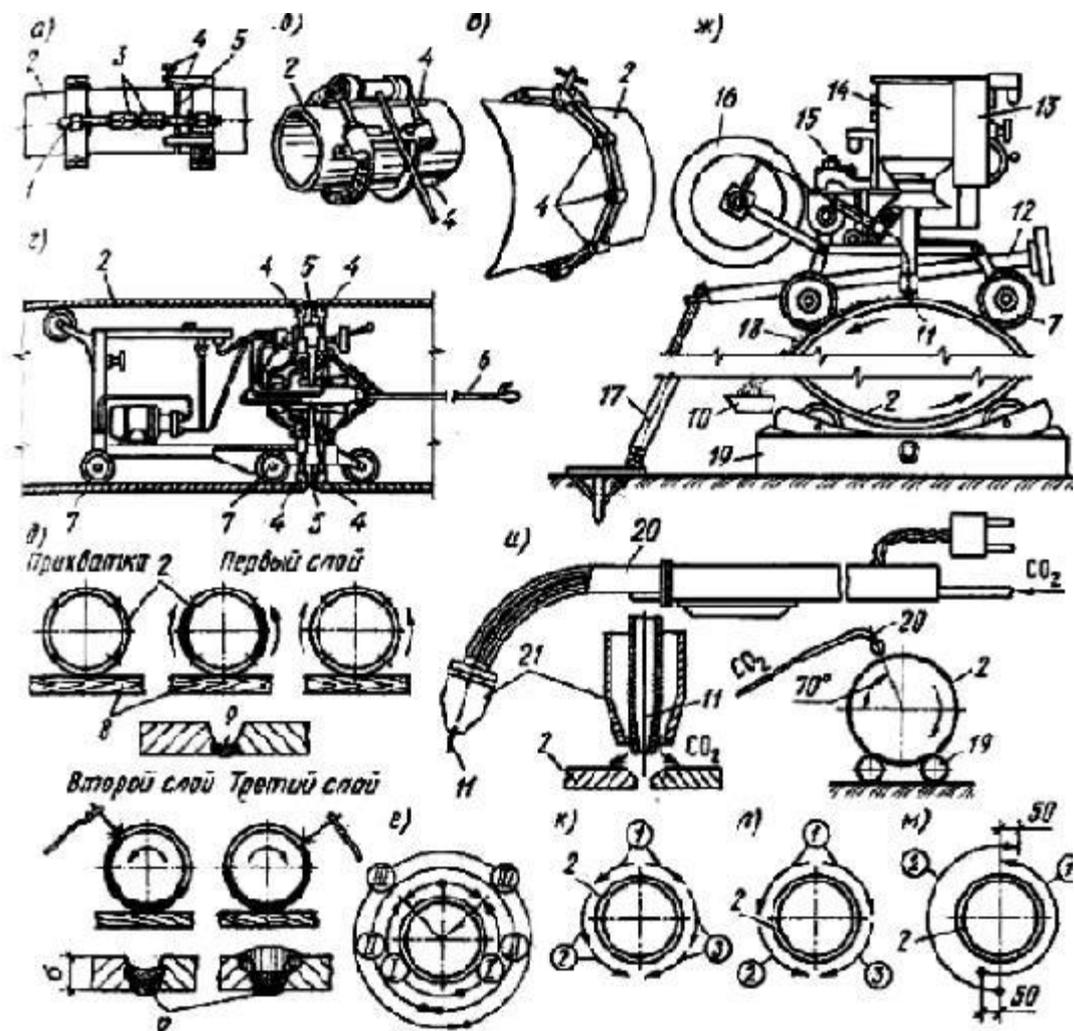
Сборка и сварка стальных труб: а, б - центраторы винтовой и эксцентриковый (для труб диаметром не более 350 мм); в - то же, наружный роликозвеньеовой (для труб 520...1020 мм); г - то же, внутренний гидравлический (для труб 520...1020 мм); д, е - последовательность операций при ручной электросварке стыков поворотным и неповоротным трехслойным швом; ж - схема применения сварочной головки ПТ-56 для поворотной сварки стыков под слоем флюса; и - то же, для
